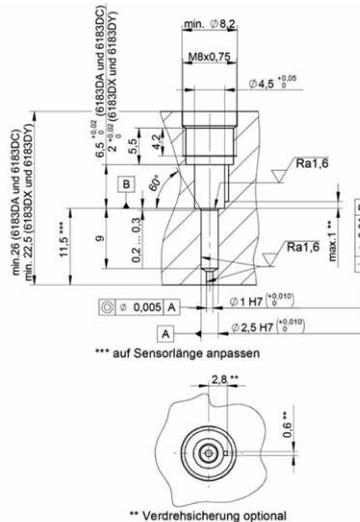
Montagebohrung für Einbau mit Montagemutter
